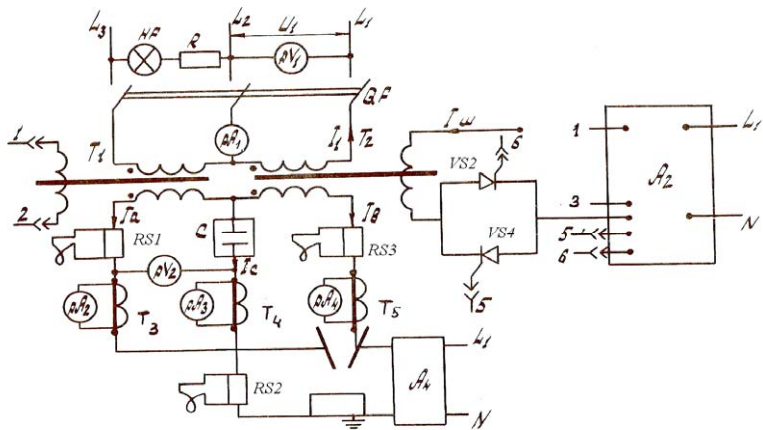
Принципиальная схема установки УДГТ-314 для сварки 3-фазной дугой
